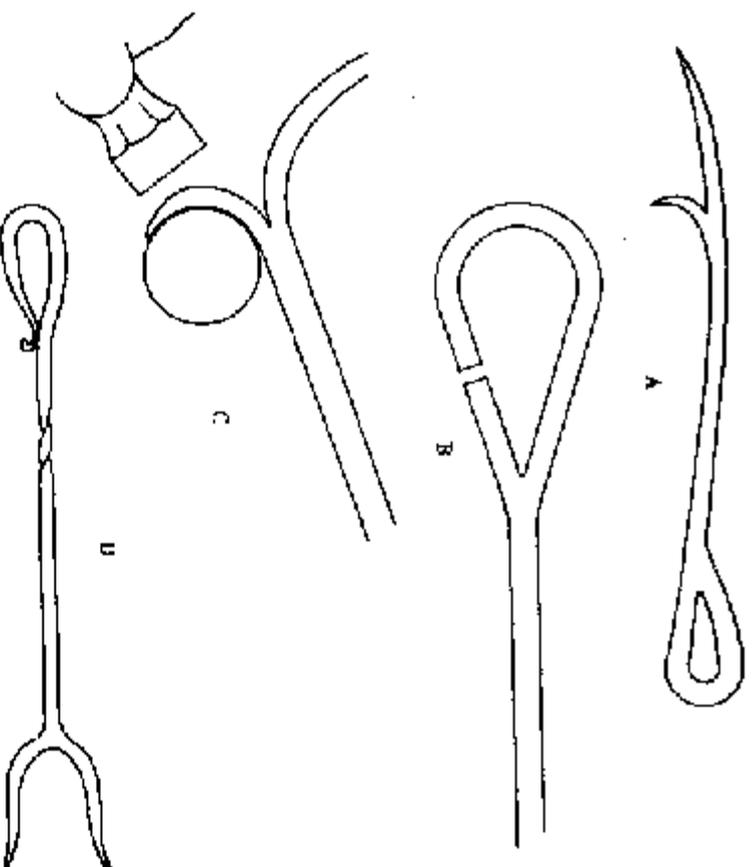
Corte de un ojo soldado (A, B, C) para hacer un arizador o una horquilla (D).
